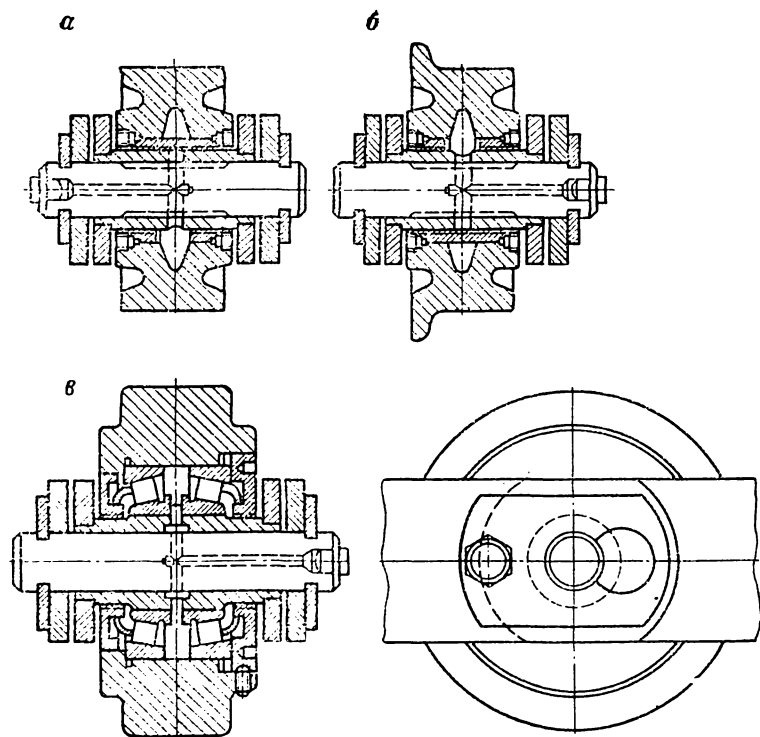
Узлы катков втулочно-катковой цепи:
